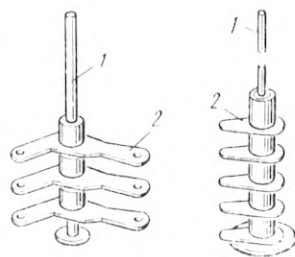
Приспособления для пайки деталей, закрепленных на штыре:
